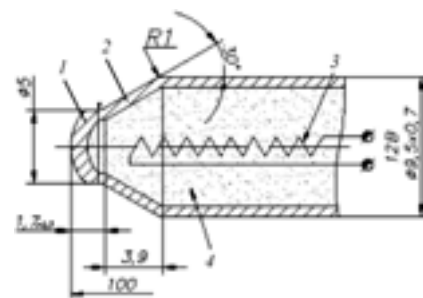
Корпус нагревательного элемента электрофакельного устройства штифтовой свечи накаливания 11.3740:
